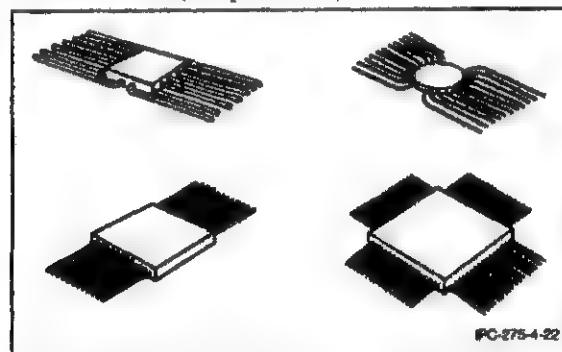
Плоские корпуса и квадратные плоские корпуса
